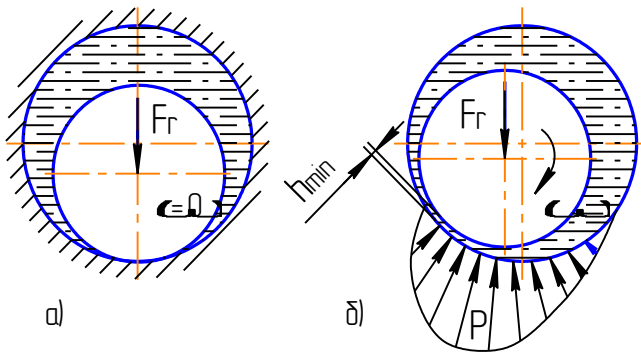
Положення вала в підшипнику й схема виникнення несучого мастильного шару
